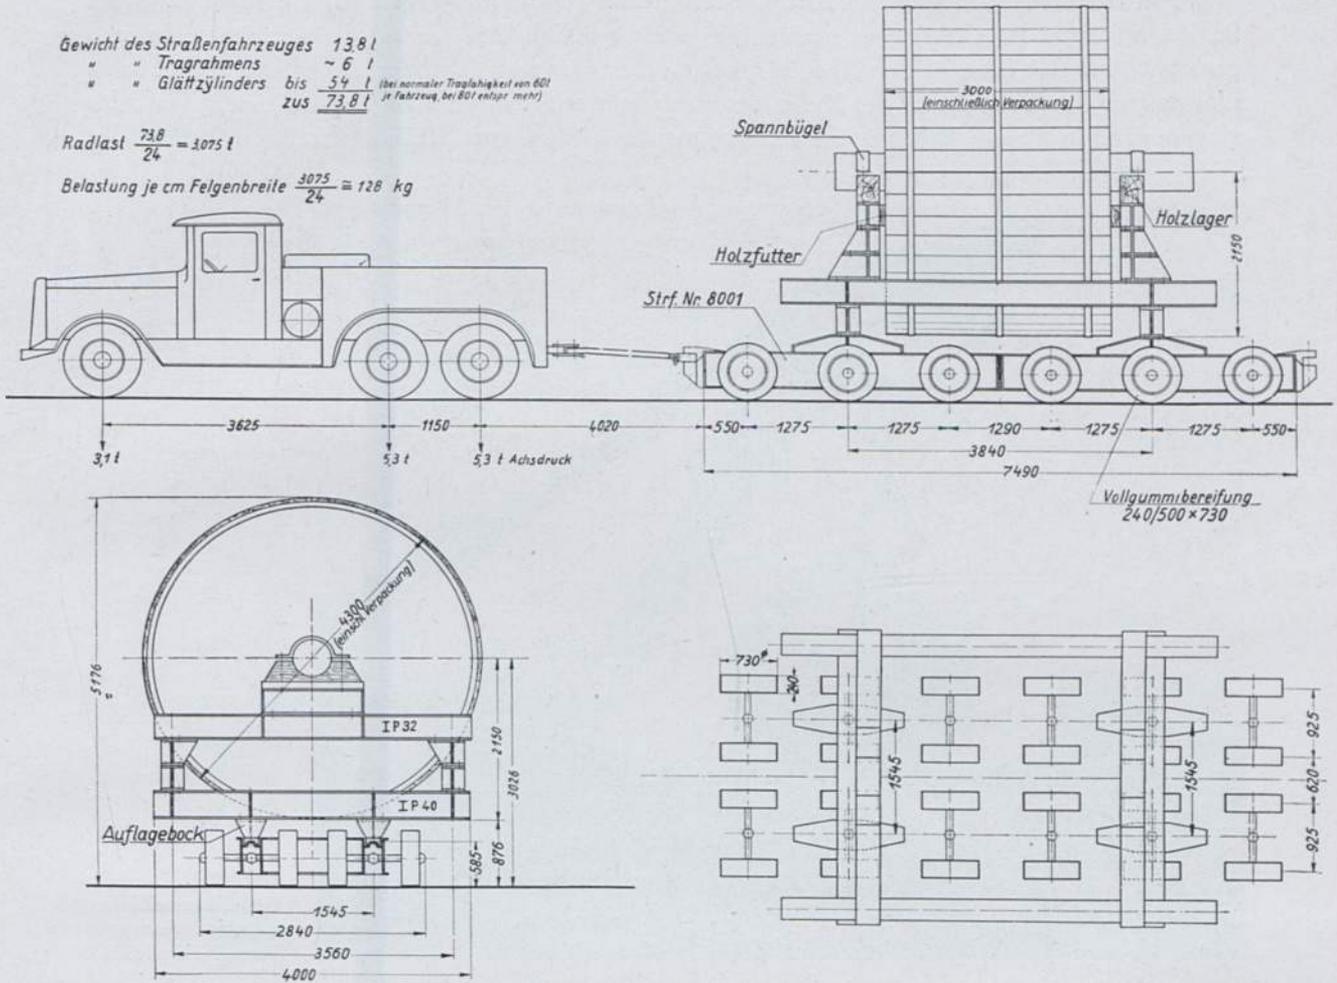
Entwurf zur Beförderung gemäß Abb. 356.
